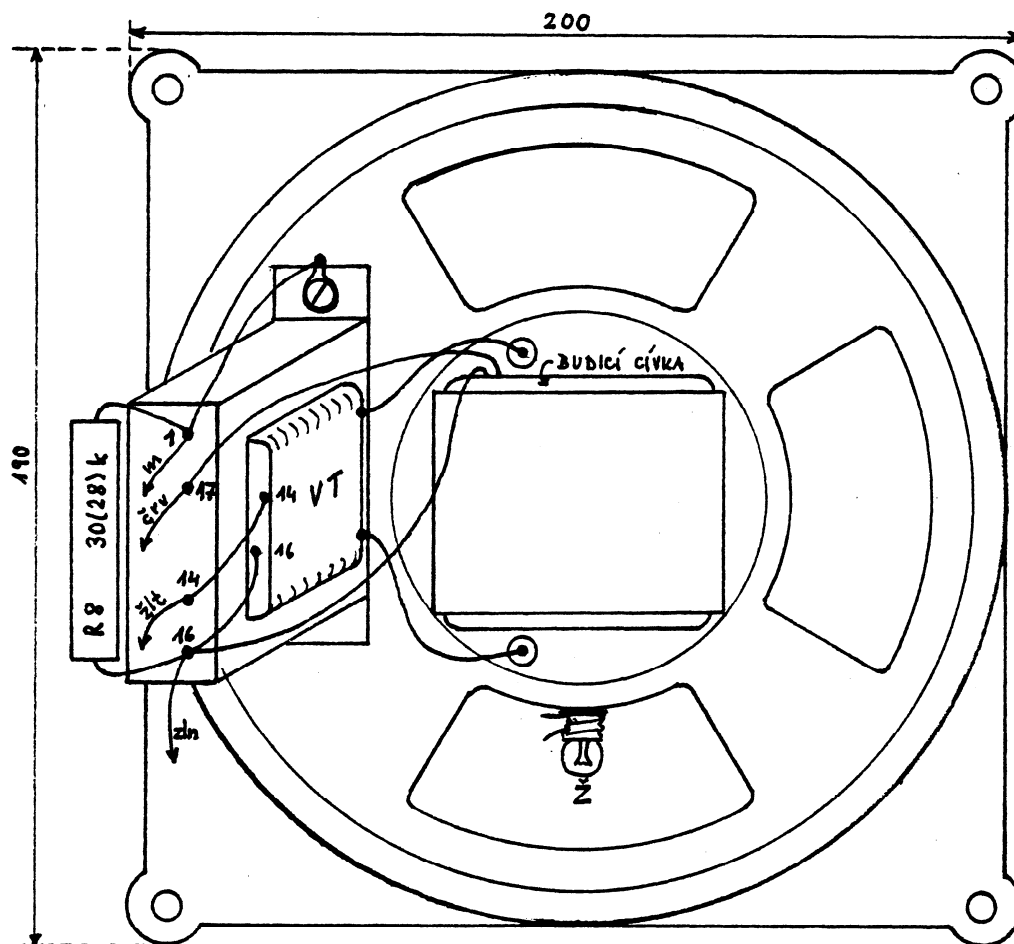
Rozmístění součástek a vedení spojů pod šasi.
